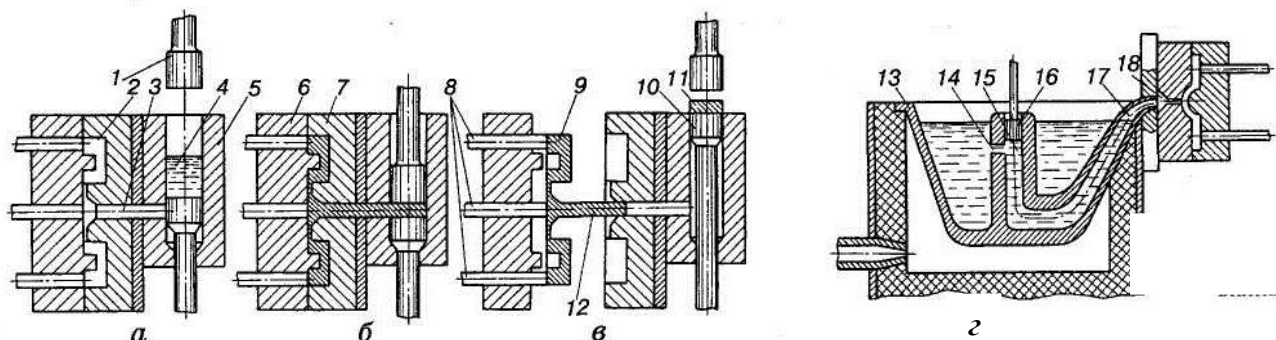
Схема роботи холодної та гарячої камери стискування: а – заливання розплавленого металу в холодну камеру; б – виливання під тиском; в – виштовхування готового виливка; г – гаряча камера стискування
